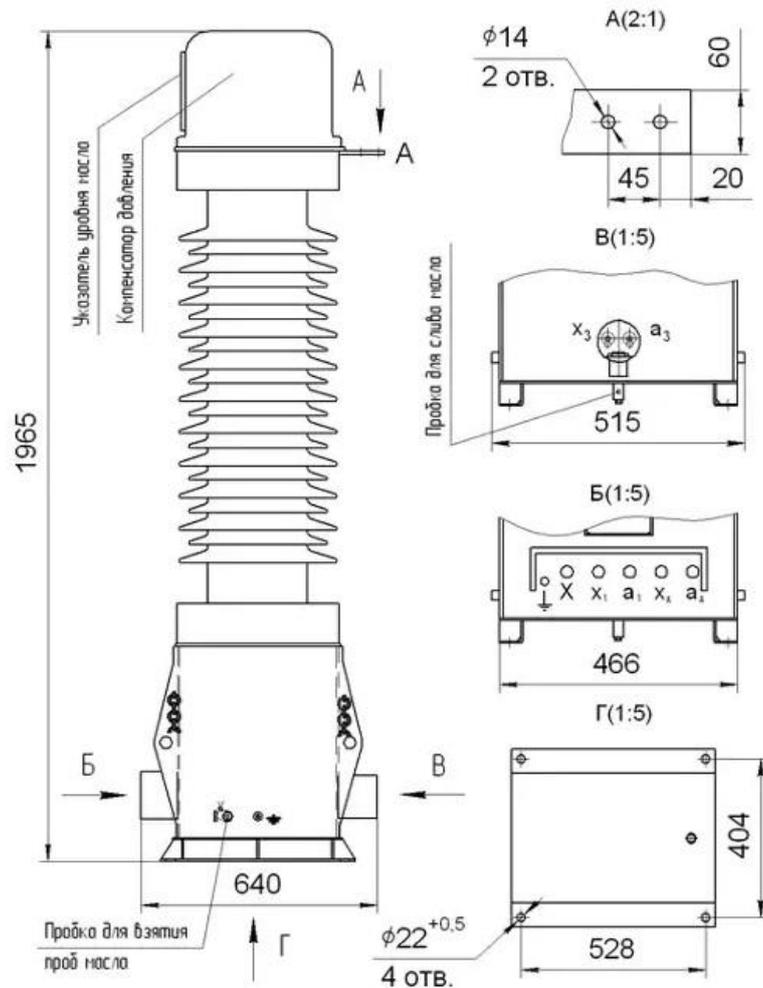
Габаритный чертеж трансформатора напряжения НАМИ – 110-УХЛ1
